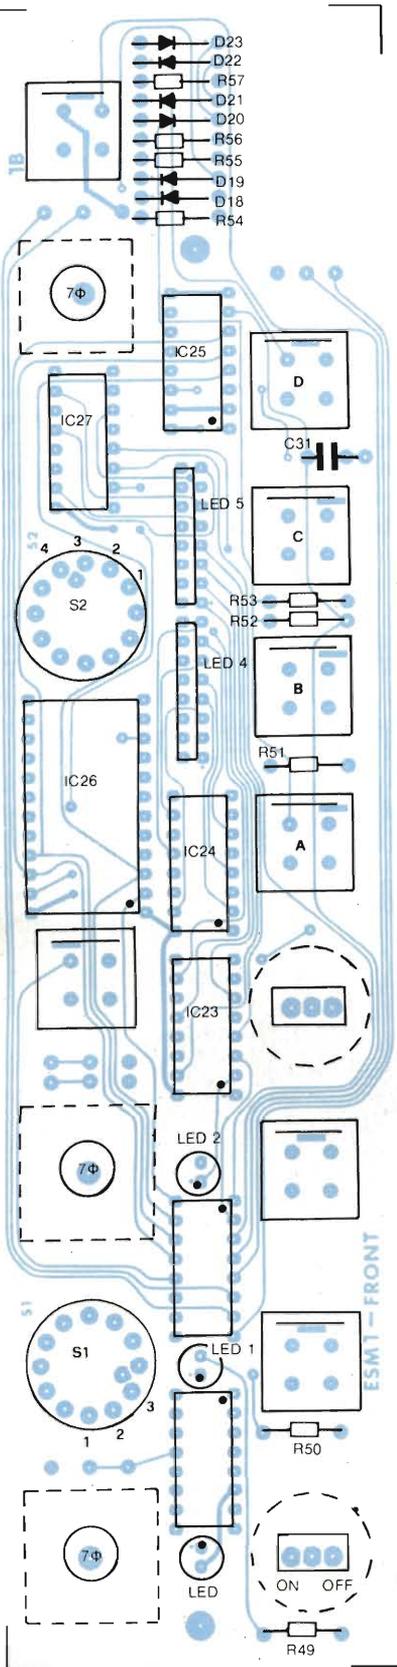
Disposizione dei componenti sul circuito stampato frontale, con tutti gli elementi di comando e gli indicatori.
